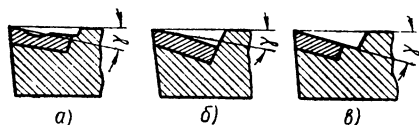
Формы передней поверхности резца с быстрорежущей пластинкой.
